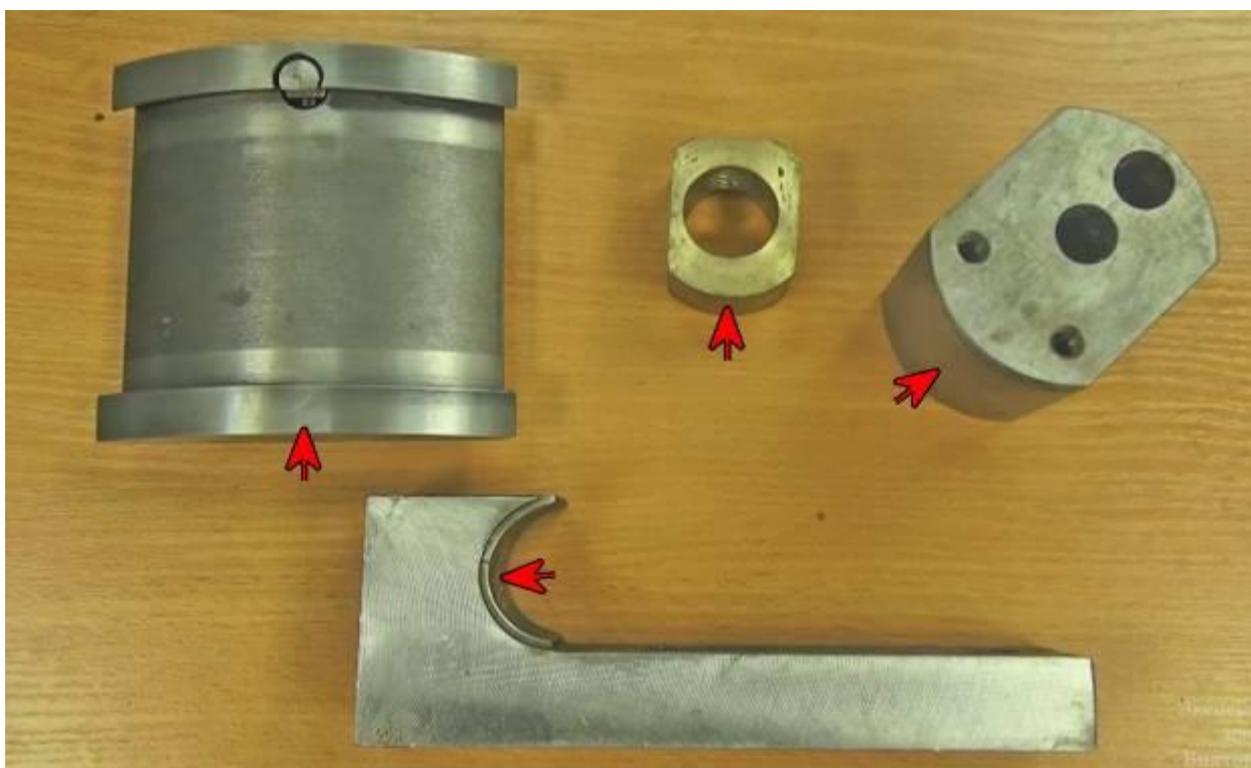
Цилиндрические валы и отверстия с полными и неполными профилями
